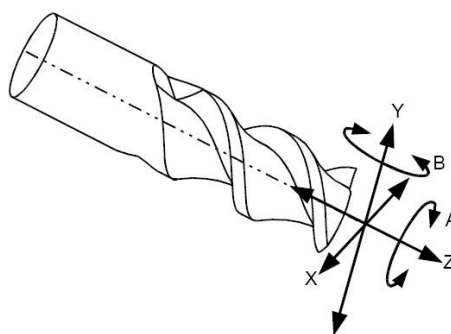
Vizualizace pohybových os (Junker Grindor Silver) pro broušení mezi hroty [14].
